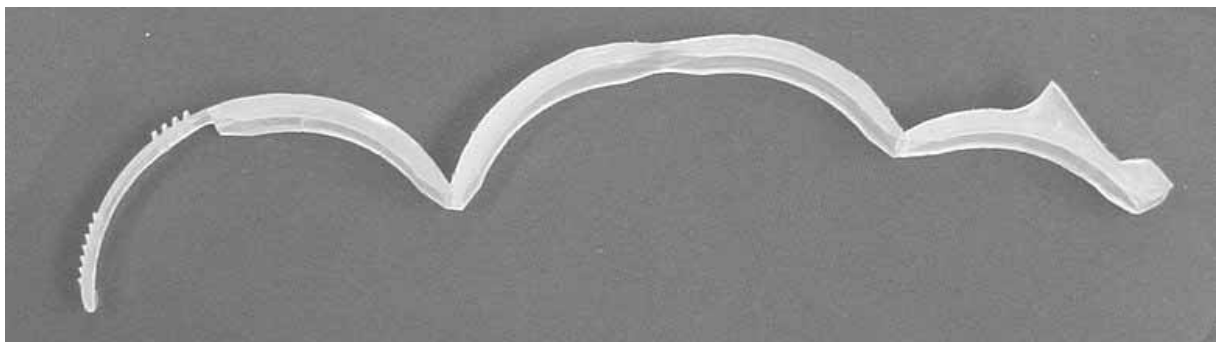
Protótipo resultante da moldagem nos moldes SL
